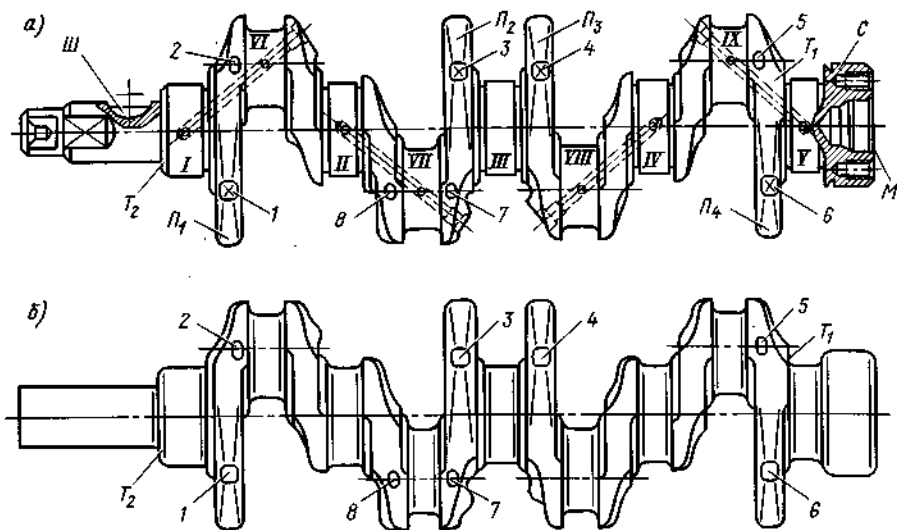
Коленчатый вал двигателя автомобиля ВАЗ-2101 (а) и его отливка (б): 1...8— опорные технологические площадки (бобышки); П<sub>1</sub>...П<sub>4</sub>— противовесы; I...V— коренные шейки; VI...IX— шатунные шейки
